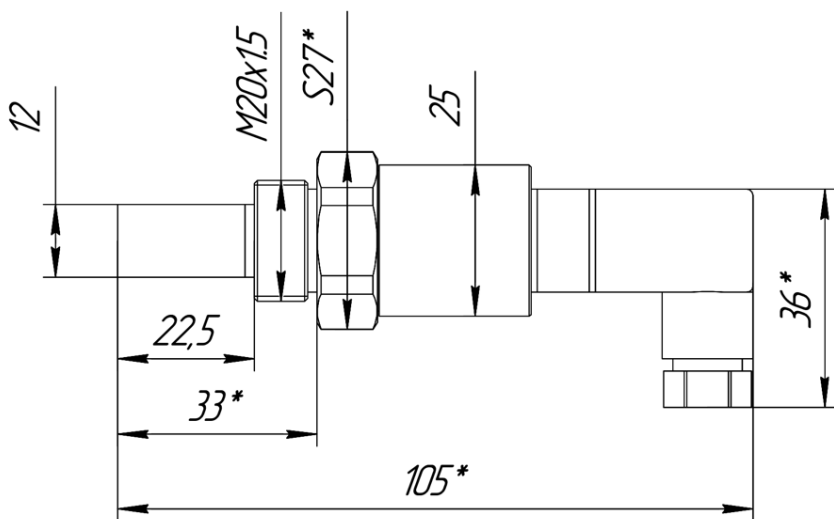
Установочные и габаритные размеры преобразователя ДТР-3-Т20-М.
